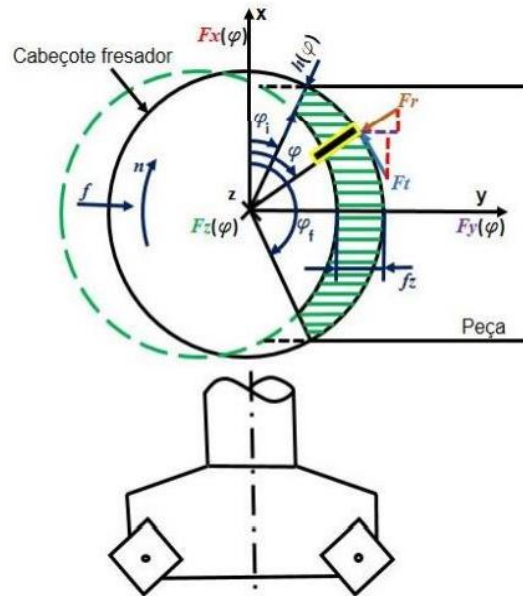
Componentes da força de usinagem no fresamento frontal [Lima et al., 2012].
